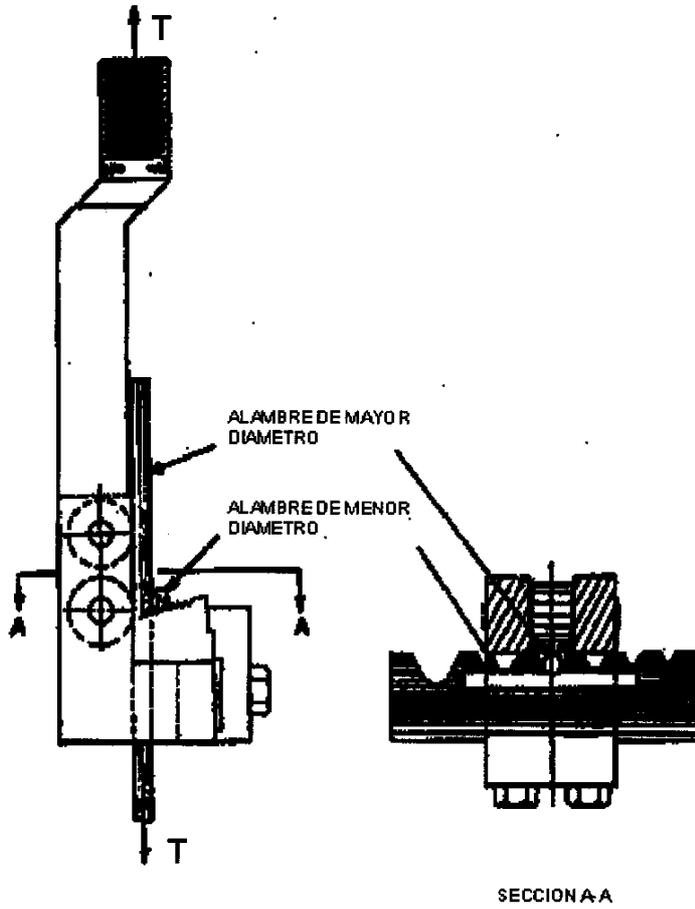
Esquema del Soporte para el Ensayo de Resistencia al Corte de la Soldadura
